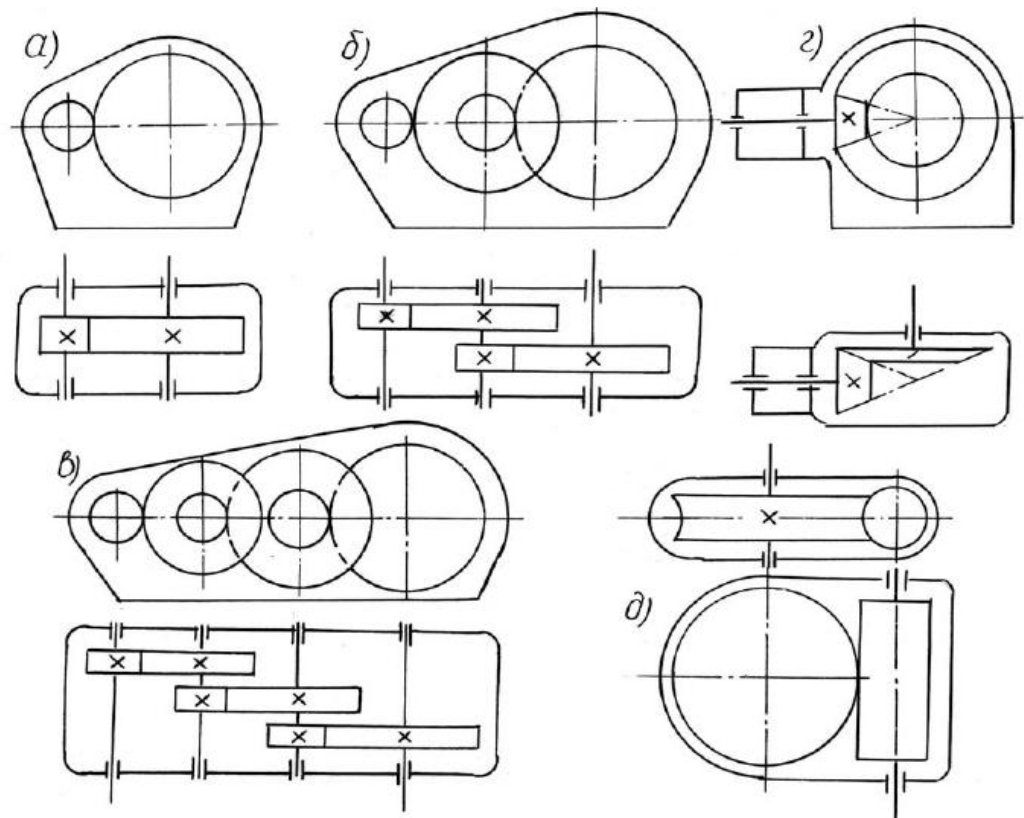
Кинематические схемы редукторов: а – цилиндрический одноступенчатый; б – цилиндрический двухступенчатый; в – цилиндрический трёхступенчатый; г – конический; д – червячный
